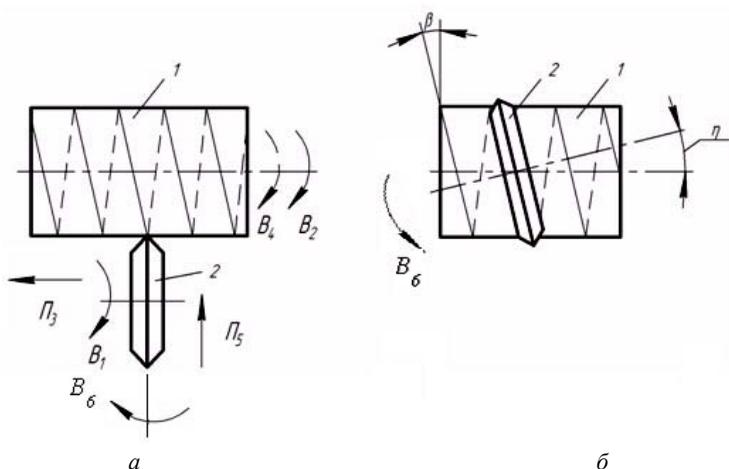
Кинематическая схема нарезания резьбы дисковой фрезой:
